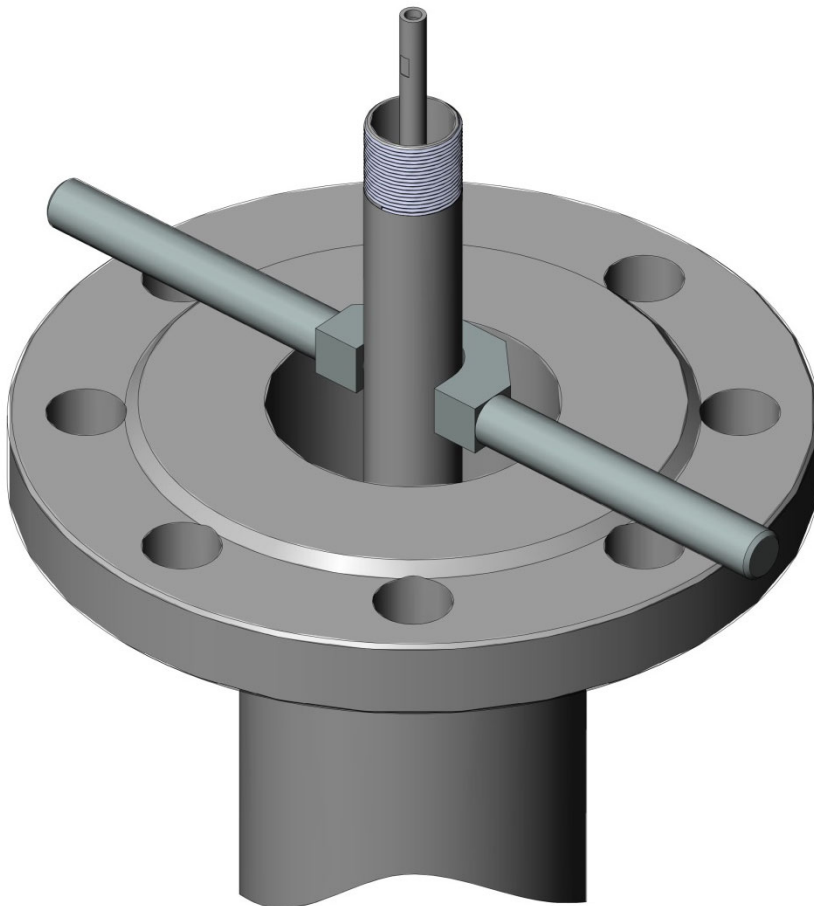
Погружение нижней секции в резервуар с опорой на приспособление
